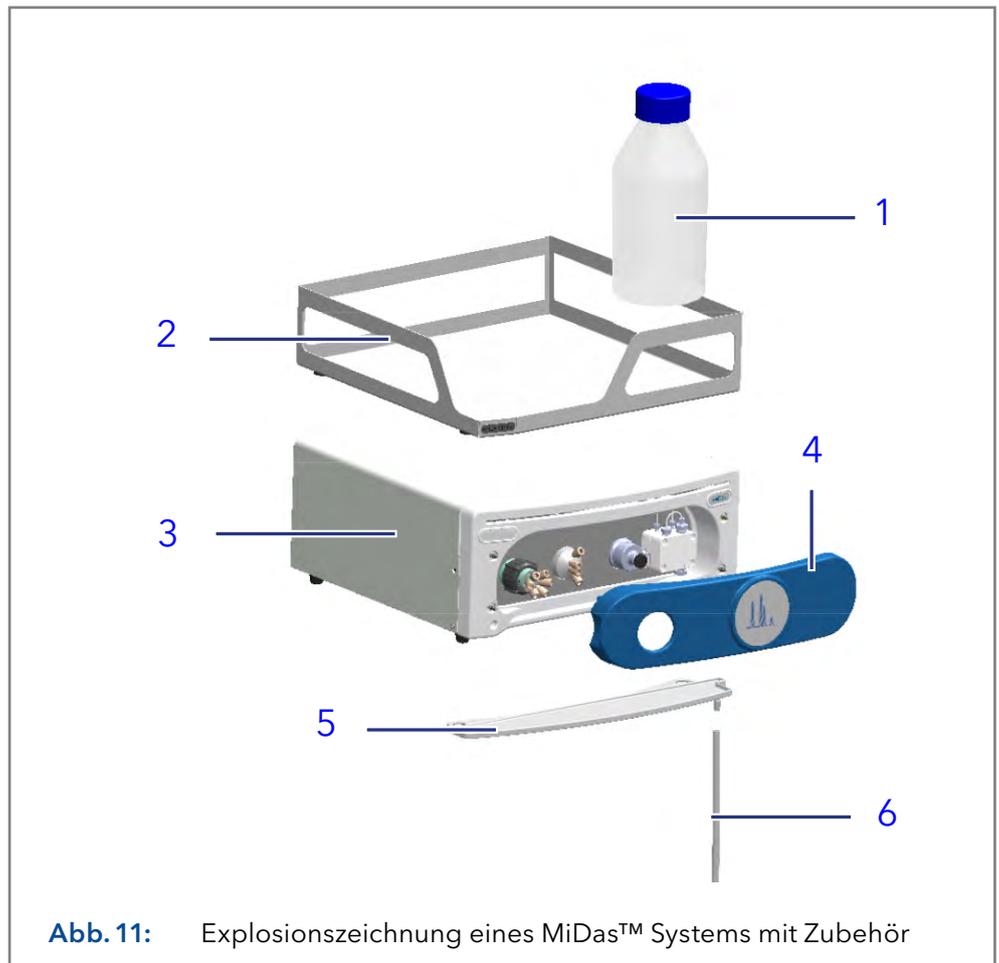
Explosionszeichnung eines MiDas™ Systems mit Zubehör
